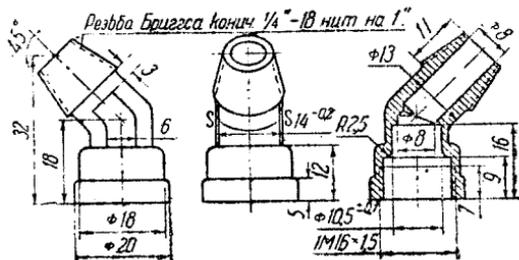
Дет. № 41180. Колено к корпусу заднего подшипника вентилятора
